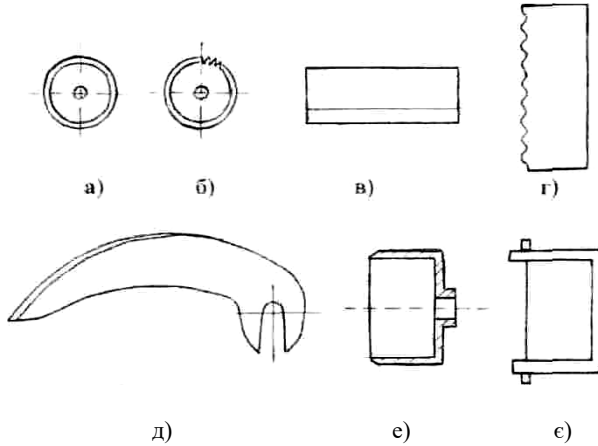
Основні форми ножів: а) гладкий дисковий; б) зубчастий дисковий; в) гладкий плоский; г) зубчастий стрічковий; д) шаблеподібний; е) горшкоподібний; е) ріжуча струна
